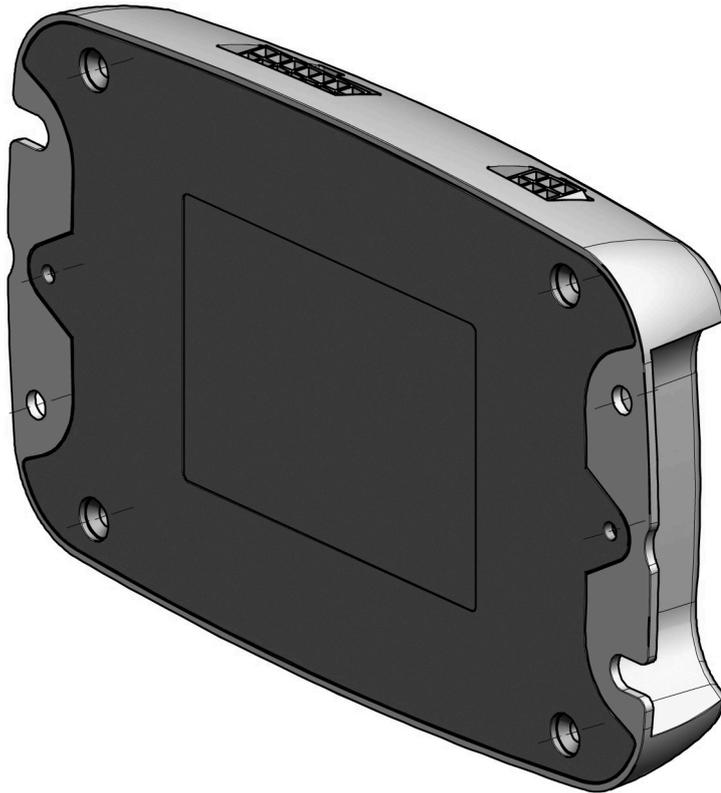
Внешний вид нижней панели корпуса основного блока.
